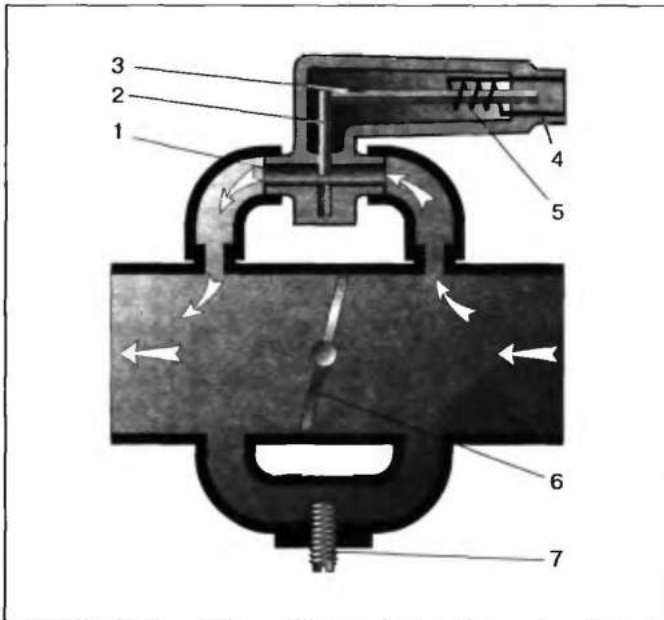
Установка и конструкция клапана дополнительного воздуха:
